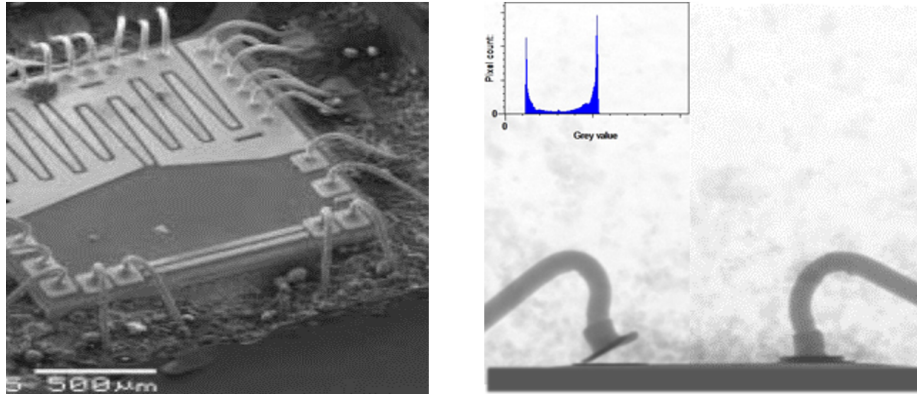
Rupture de contact causé par un stress thermo-mécanique
